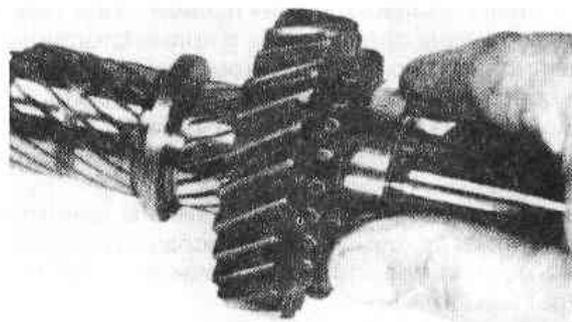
Установка шестерни второй передачи (коробка передач С) (Разд.6)
